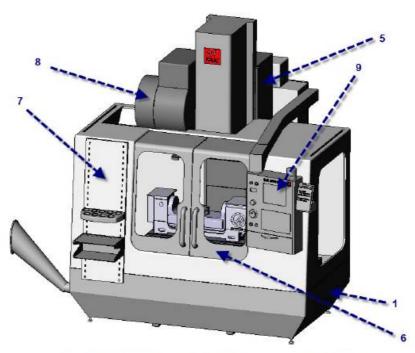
Корпус вертикально-фрезерного станка с ЧПУ
